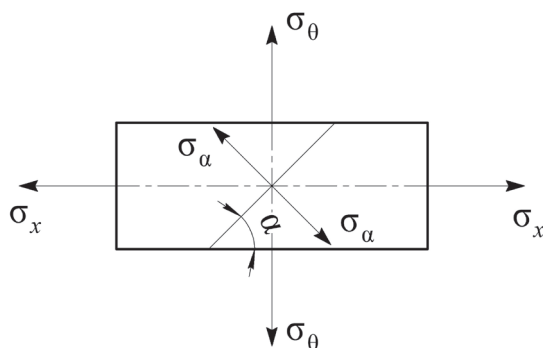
Схема напряжений в элементе и сварочном шве трубы
